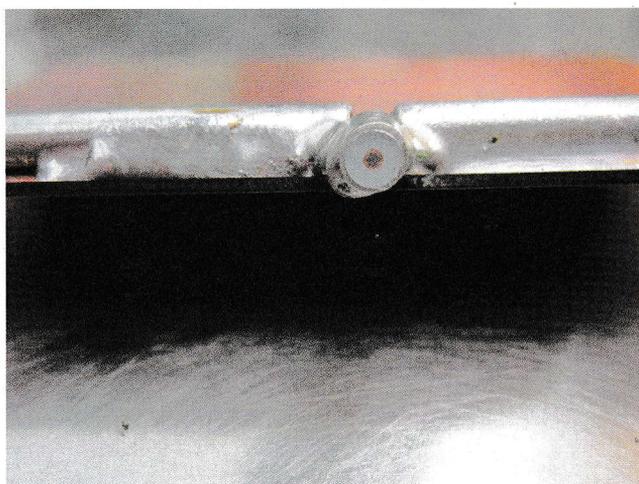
Das Ablängen der Stichleitung aus Bild 3 ergibt mit einer kleinen, hochoberflächigen Trennscheibe einen sauberen Schnitt
